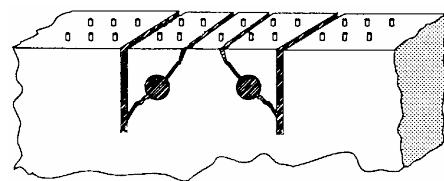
Прессовые инструменты слишком близки к прорезям
